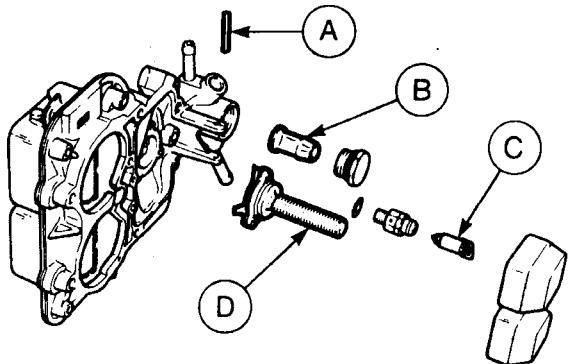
Детали верхней части корпуса - карбюратор WEBER. А - Ось поплавка. В - Фильтр. С - Игольчатый клапан. D - Экономайзер.
